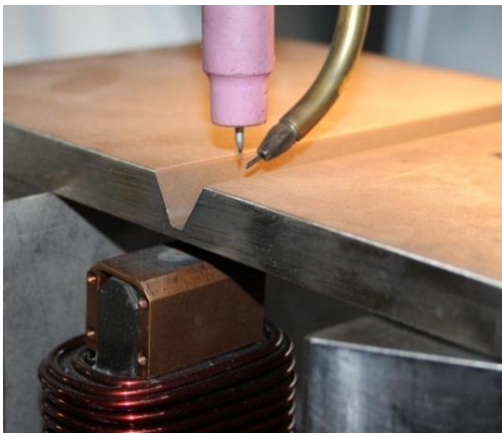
Detailaufnahme experimenteller Aufbau mit Elektromagnet, Schweißbrenner, Drahtzufuhr, Nahtgeometrie funkenerosiv hergestellt
